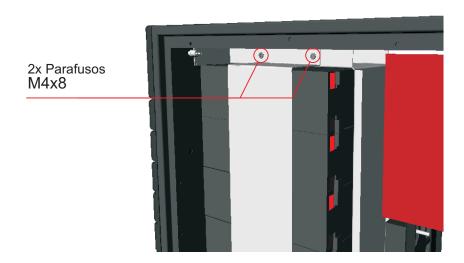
Inserir o suporte e fixar os parafusos M4X8
